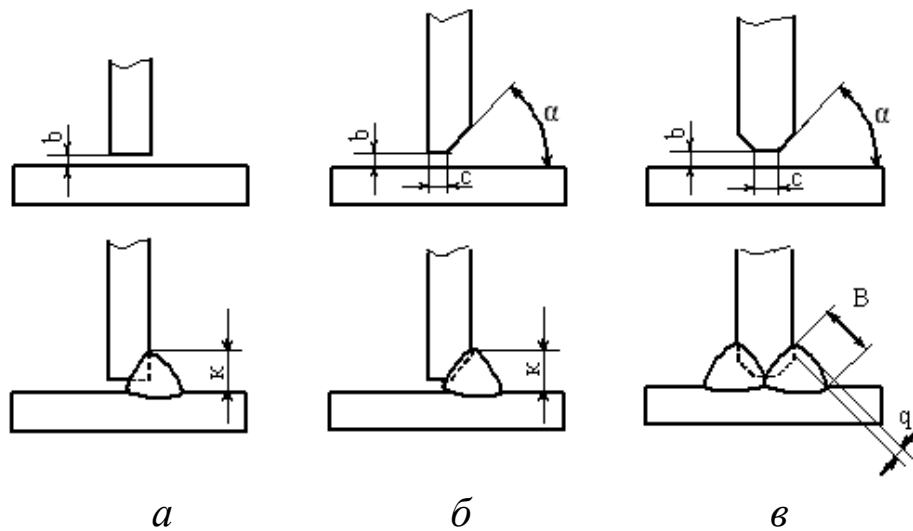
Форма разделки кромок при сварке угловых швов: *a* – без разделки; *б* и *в* – с разделкой
